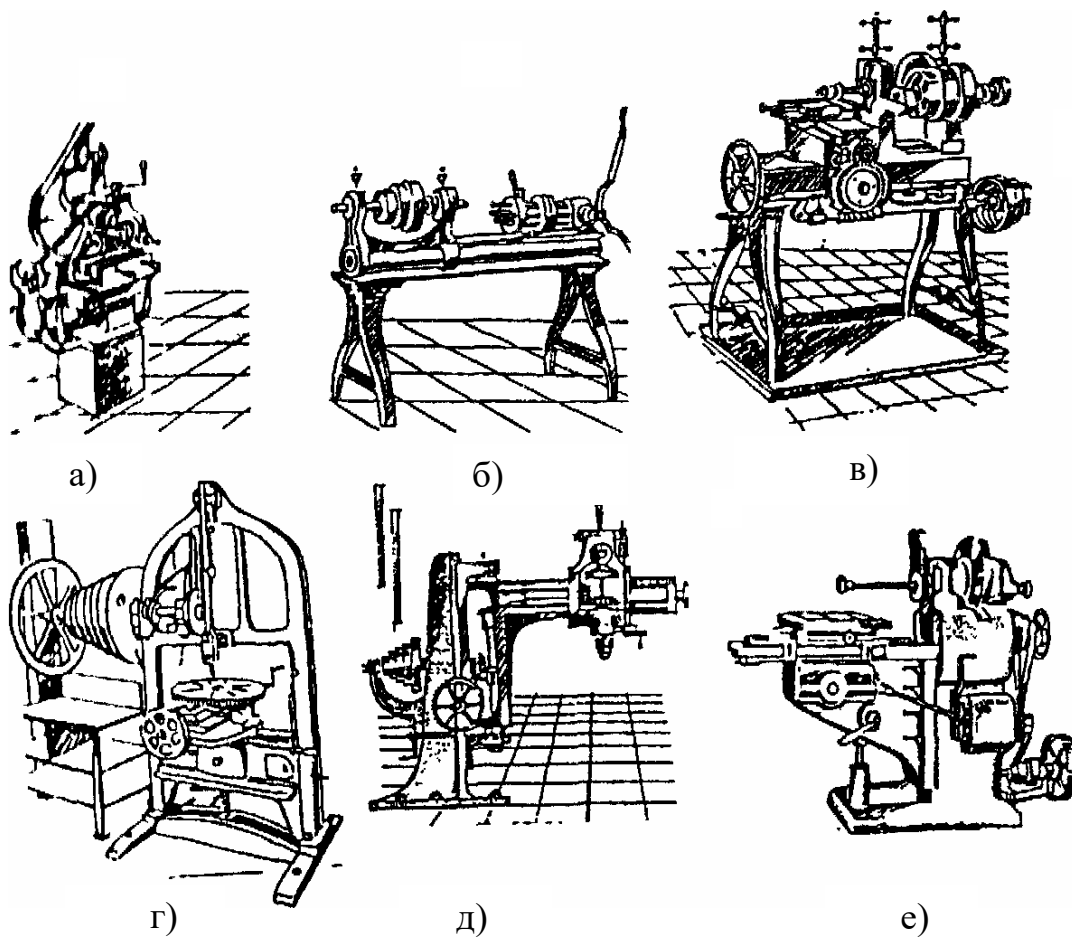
Металорізальні верстати XIX в.: а - фрезерний верстат Г.Силвера (1835 р.); б - револьверний верстат С. Фриша (1848 р.), в - фрезерний верстат Ф. Хау і Е. Рутта (1848 р.); г - довбальний верстат (50-і рр. XIXв.), д - свердлильний верстат (кінець XIX в.); е - фрезерний верстат (кінець XIX в.)
